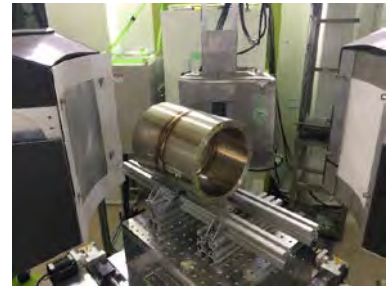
冷却系配管を模擬した実機部分模擬用溶接試験体（TIG 溶接後）の外観
